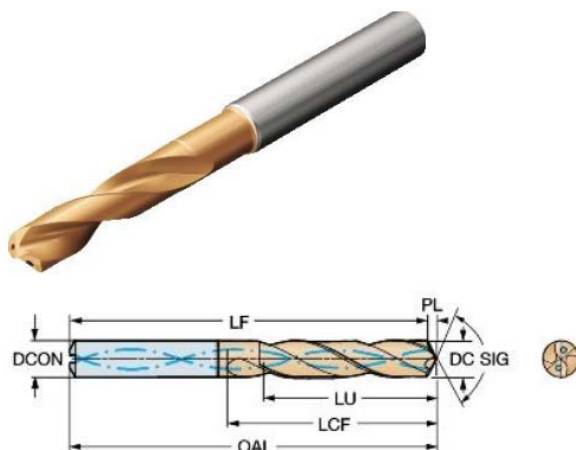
Сверло 460.1-0615-031A1-XM GC34
